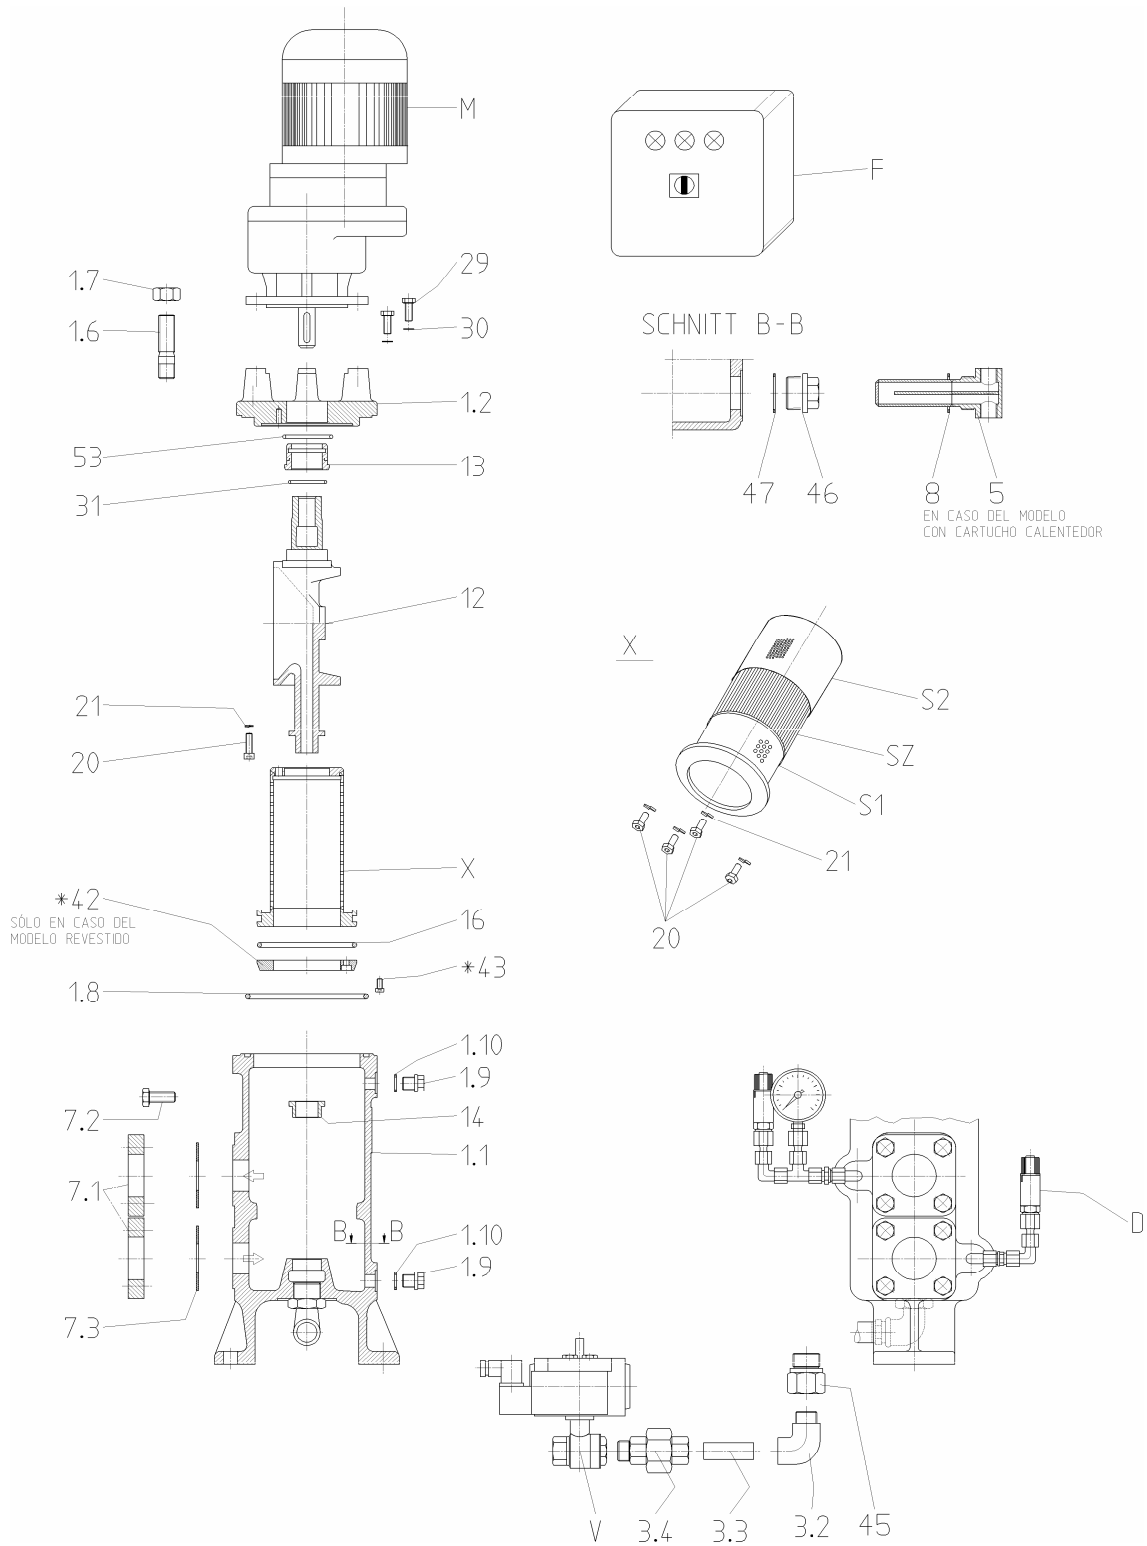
Esquema detallada de las piezas R5-8 DN32 -50
